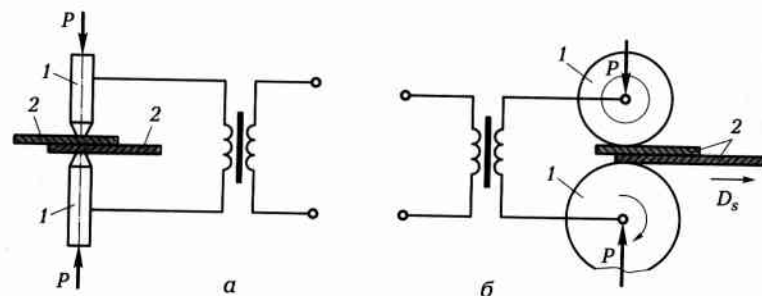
Схемы точечной (а) и шовной (б) контактной сварки: 1 — электроды; 2 — заготовки; P — прикладываемое усилие; D_s — движение подачи
